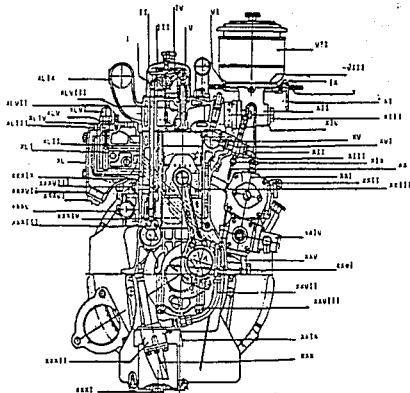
SECCION FRONTAL DE UN MOTOR DIESEL DE 4 CILINDROS
